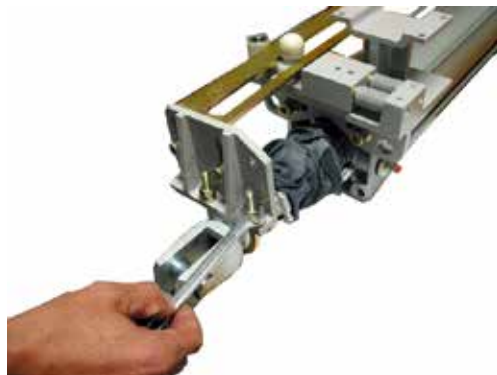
Desmontagem do Ímã do Suporte
